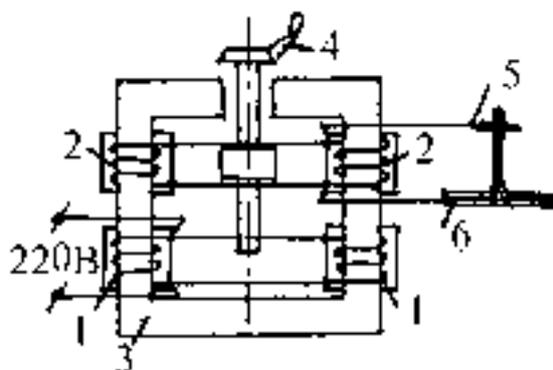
Принцип работы сварочного трансформатора
